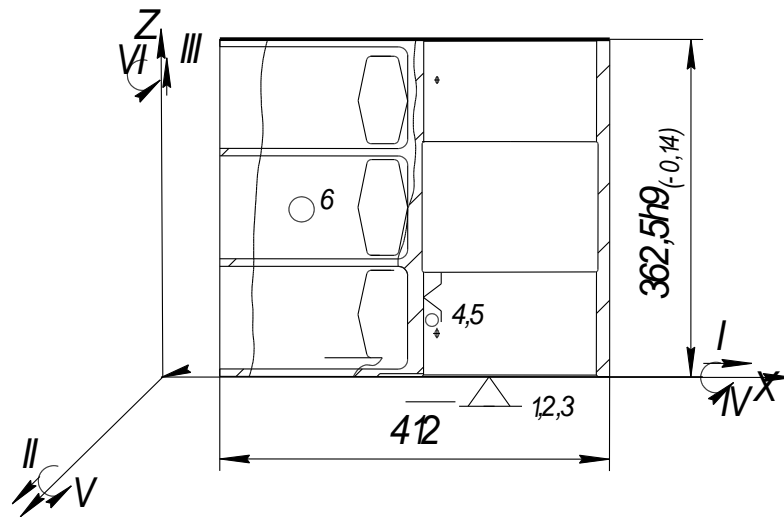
Схема базування на фрезерній операції (Установ А).
